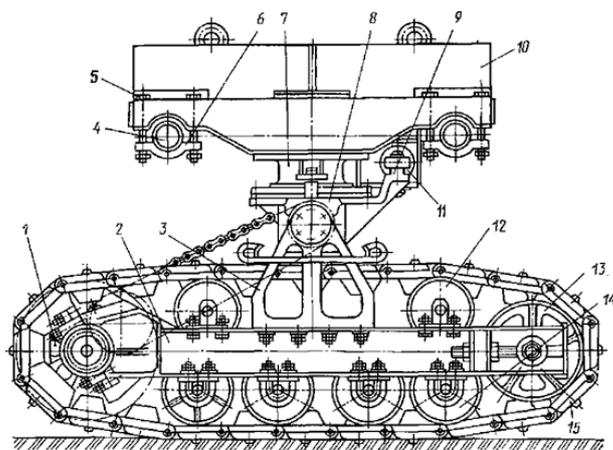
Установка вспомогательной гусеницы каналоочистителя МР-15:
